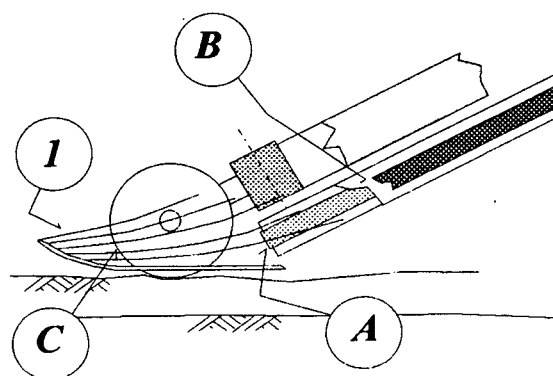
Detalhe do sistema de levantamento das ramas
